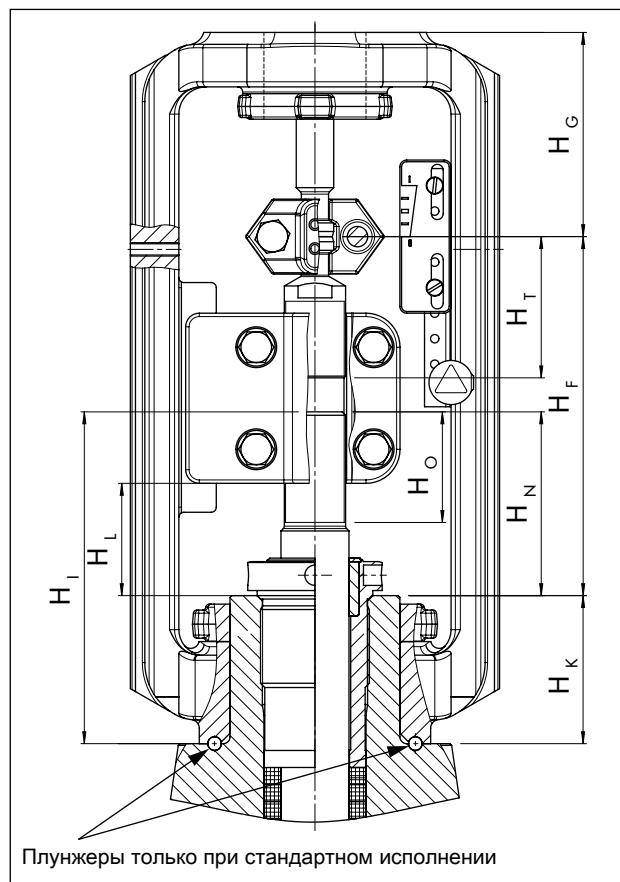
Чертеж с монтажными размерами для пневматических приводов тип 3271 и тип 3277
